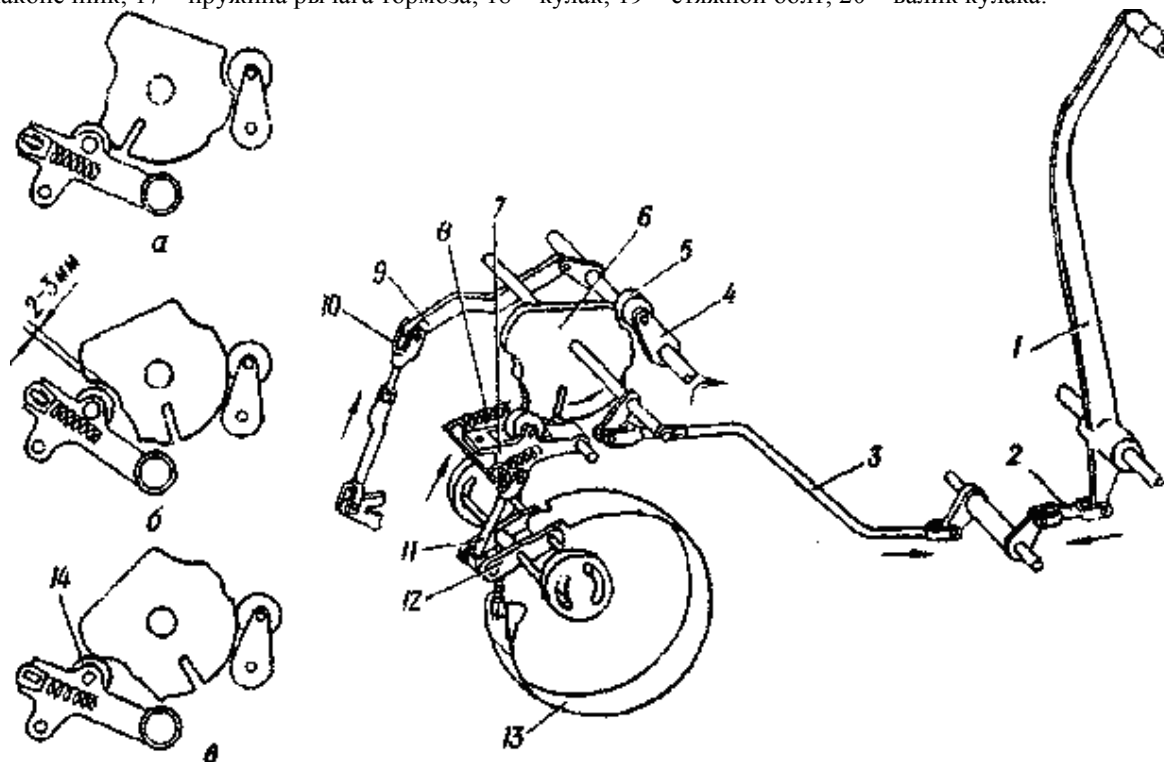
Схема привода управления планетарно-фрикционными механизмами поворота:
